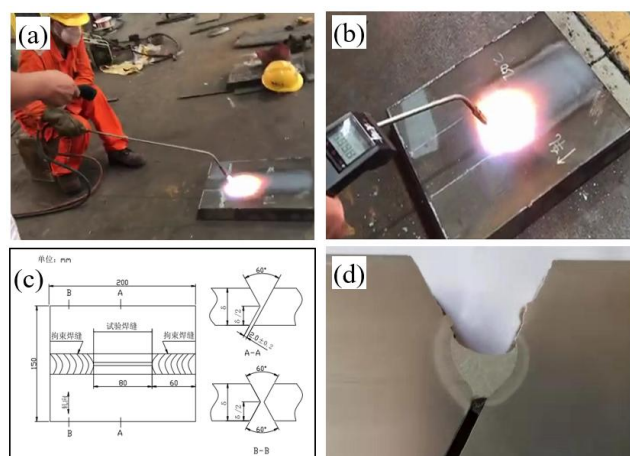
焊接热矫正试验 (a-b)，斜 Y 坡口焊接裂纹试验的样品尺寸图 (c) 和实际试件图 (d)
